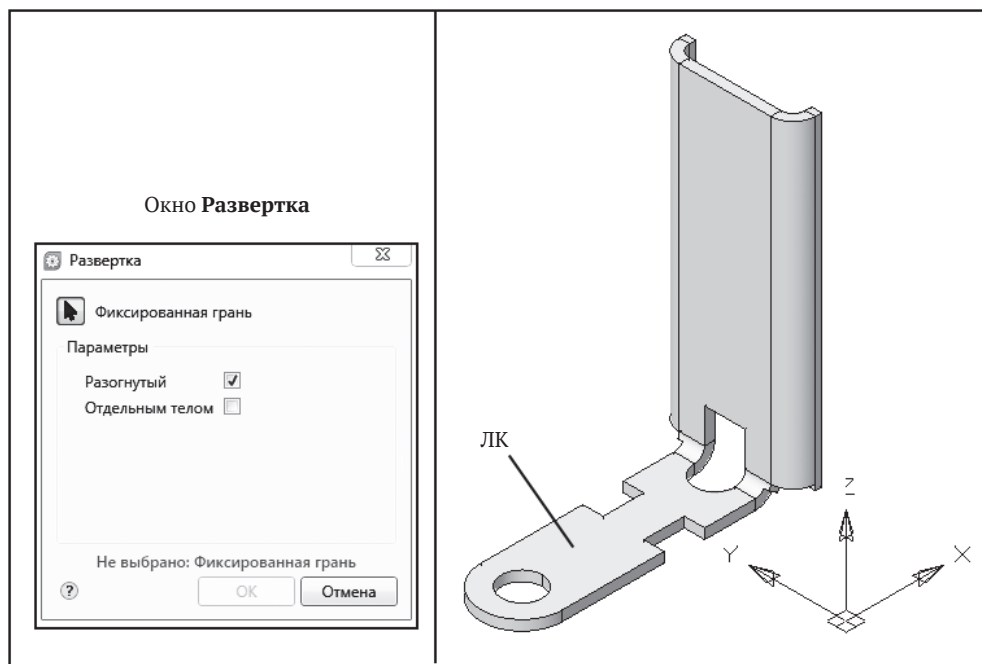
Выбор грани на 3D-модели детали «Кронштейн» для построения развертки поверхности
